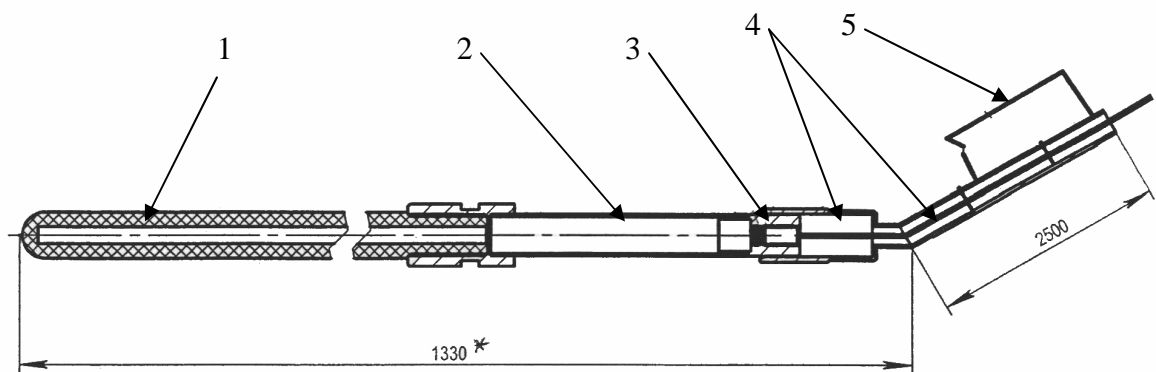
Інший варіант конструкції експериментальної установчої арматури із закритим зондом
